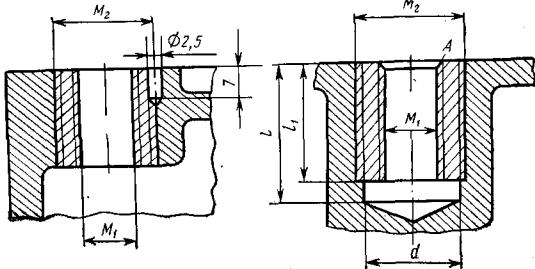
Ввертыши для ремонта резьбовых отверстий
